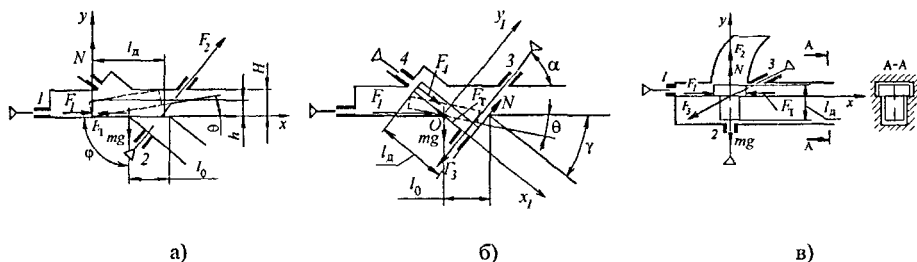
Расчетные схемы силового воздействия струй для пластин и ступенчатых деталей
